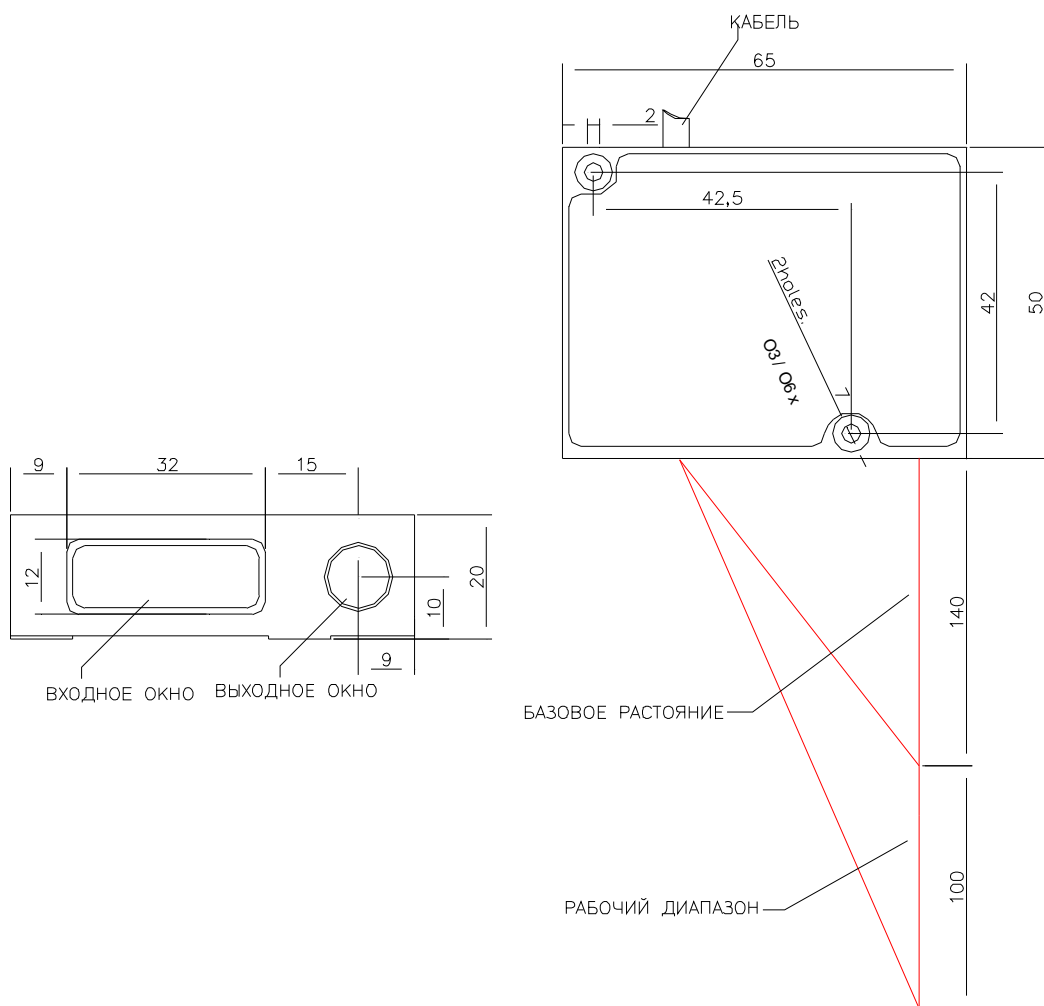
Установочные и габаритные размеры лазерного датчика серии РФ603
